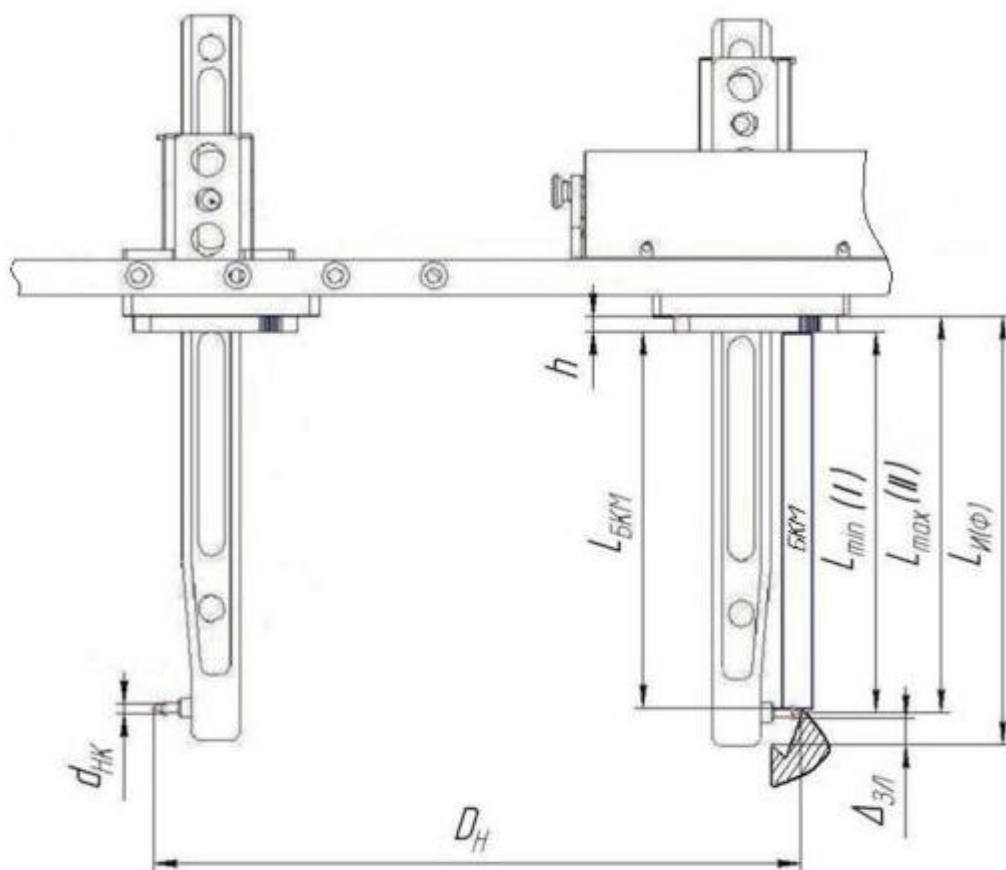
Схема настройки вылета штанг индикаторного прибора со ступенчатыми сдвижными упорами для измерения конусности уплотнительной расточки по блоку концевых мер (БKM)
